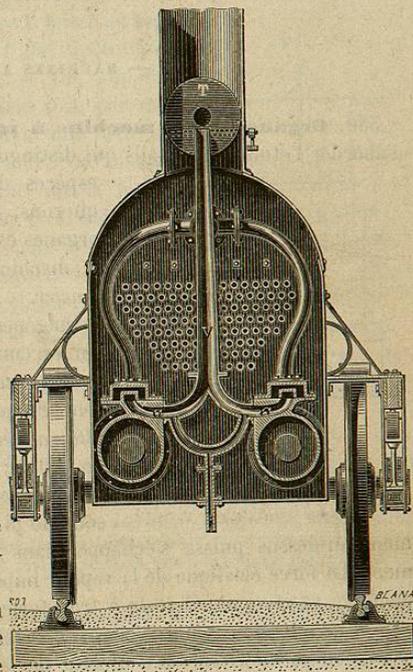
Coupe transversale passant par la boîte à fumée.
